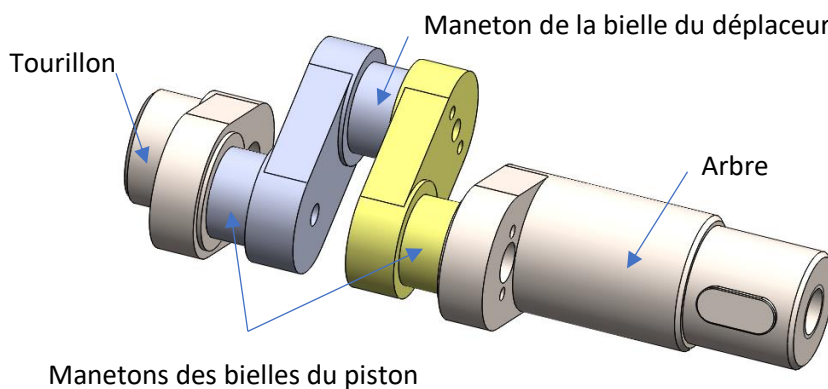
vilebrequin assemblé de la machine Stirling bêta.
